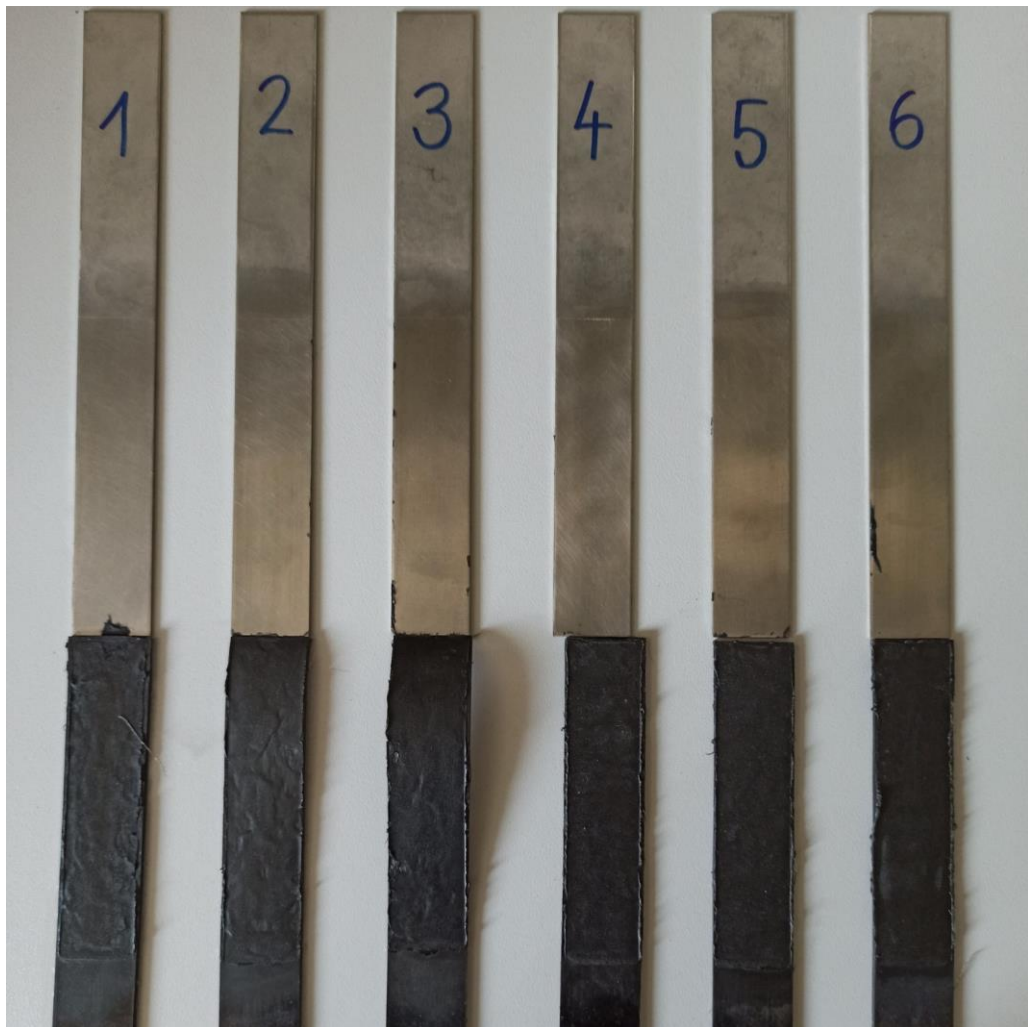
Vzorky po odlupování – Scotch-Weld™ 4799 – nezbroušená pryž
